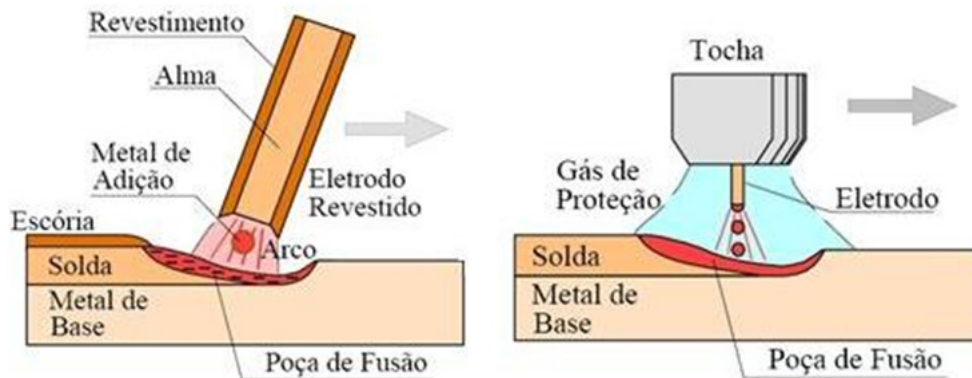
Soldagem por fusão (eletrodo revestido e MIG) <sup>(1)</sup>.
